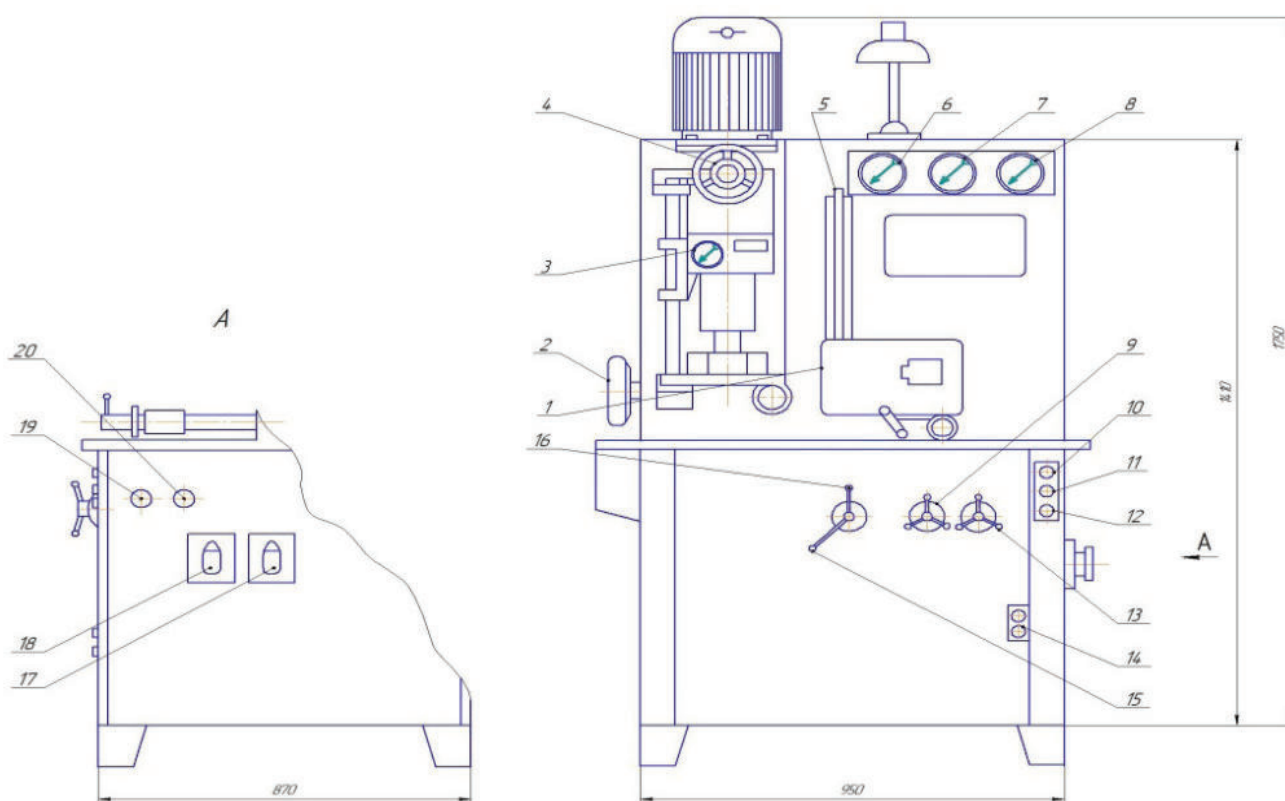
Стенд для испытания и обкатки агрегатов системы смазки двигателей
